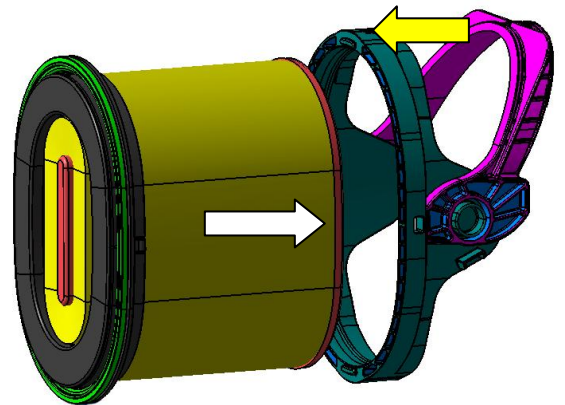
Estribo de sujeción IQORON tamaño constructivo 10 - 14
